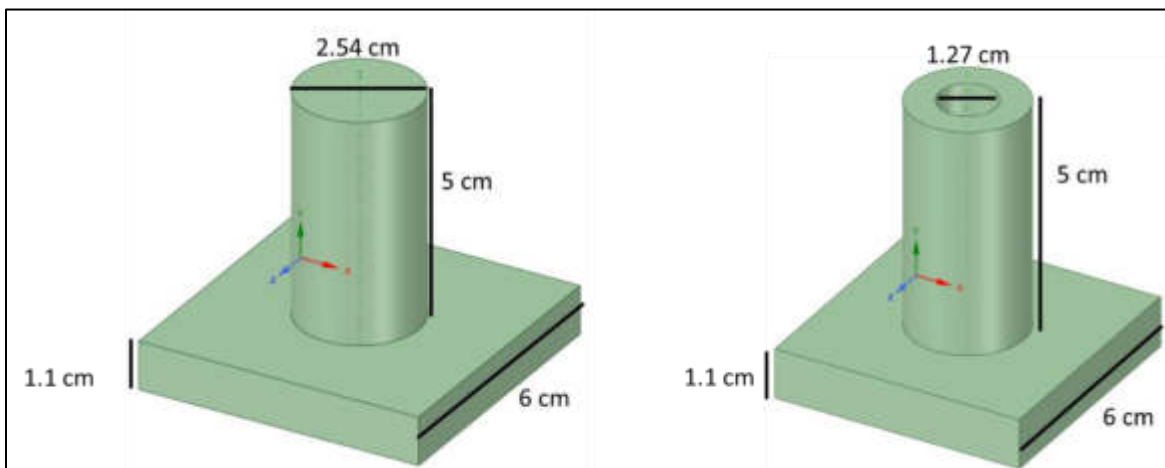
Diseño de la soldadura: Diseño de la izquierda soldadura tipo 1; diseño de la derecha soldadura tipo 2
